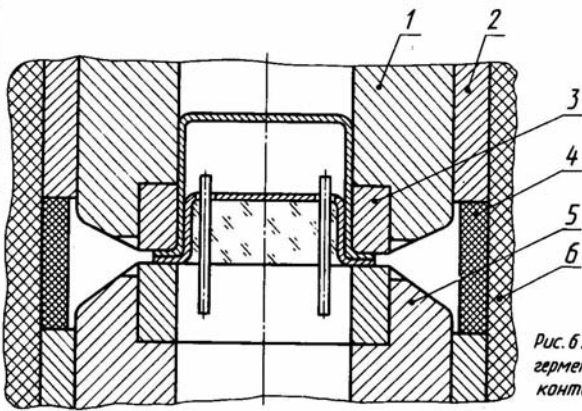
Сварочный инструмент для герметизации корпусов контурной контактной сваркой
